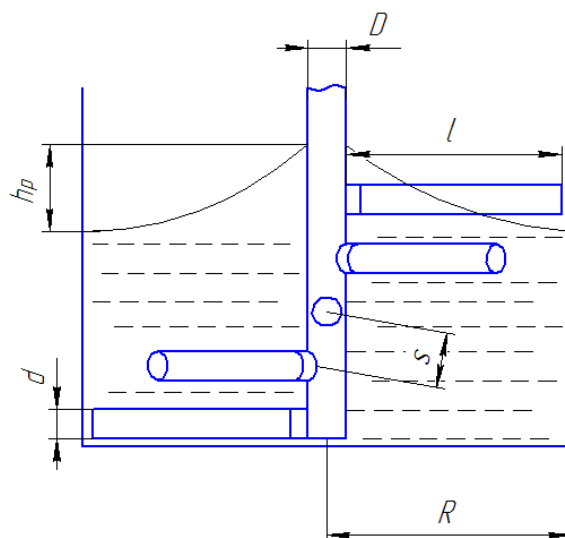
Схема экспериментально-опытного объемно-винтового рабочего органа: D – диаметр месильного вала; l – длина лопасти; S – шаг установки лопастей на месильном валу; d – диаметр лопасти; R – радиус дежи; h_p – резервный запас дежи по высоте
